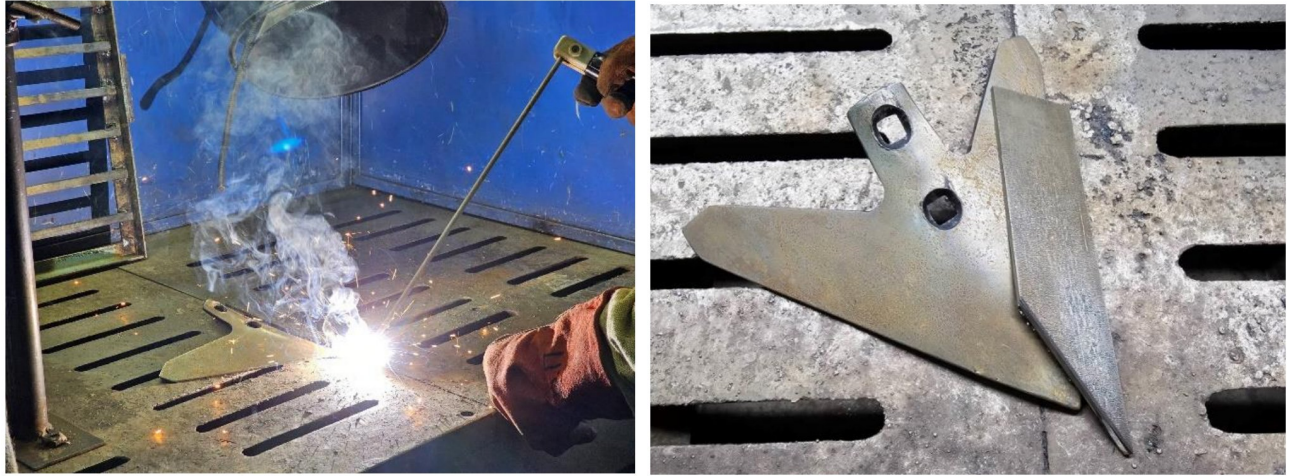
Процес приварювання пластин із низьколегованої сталі.
